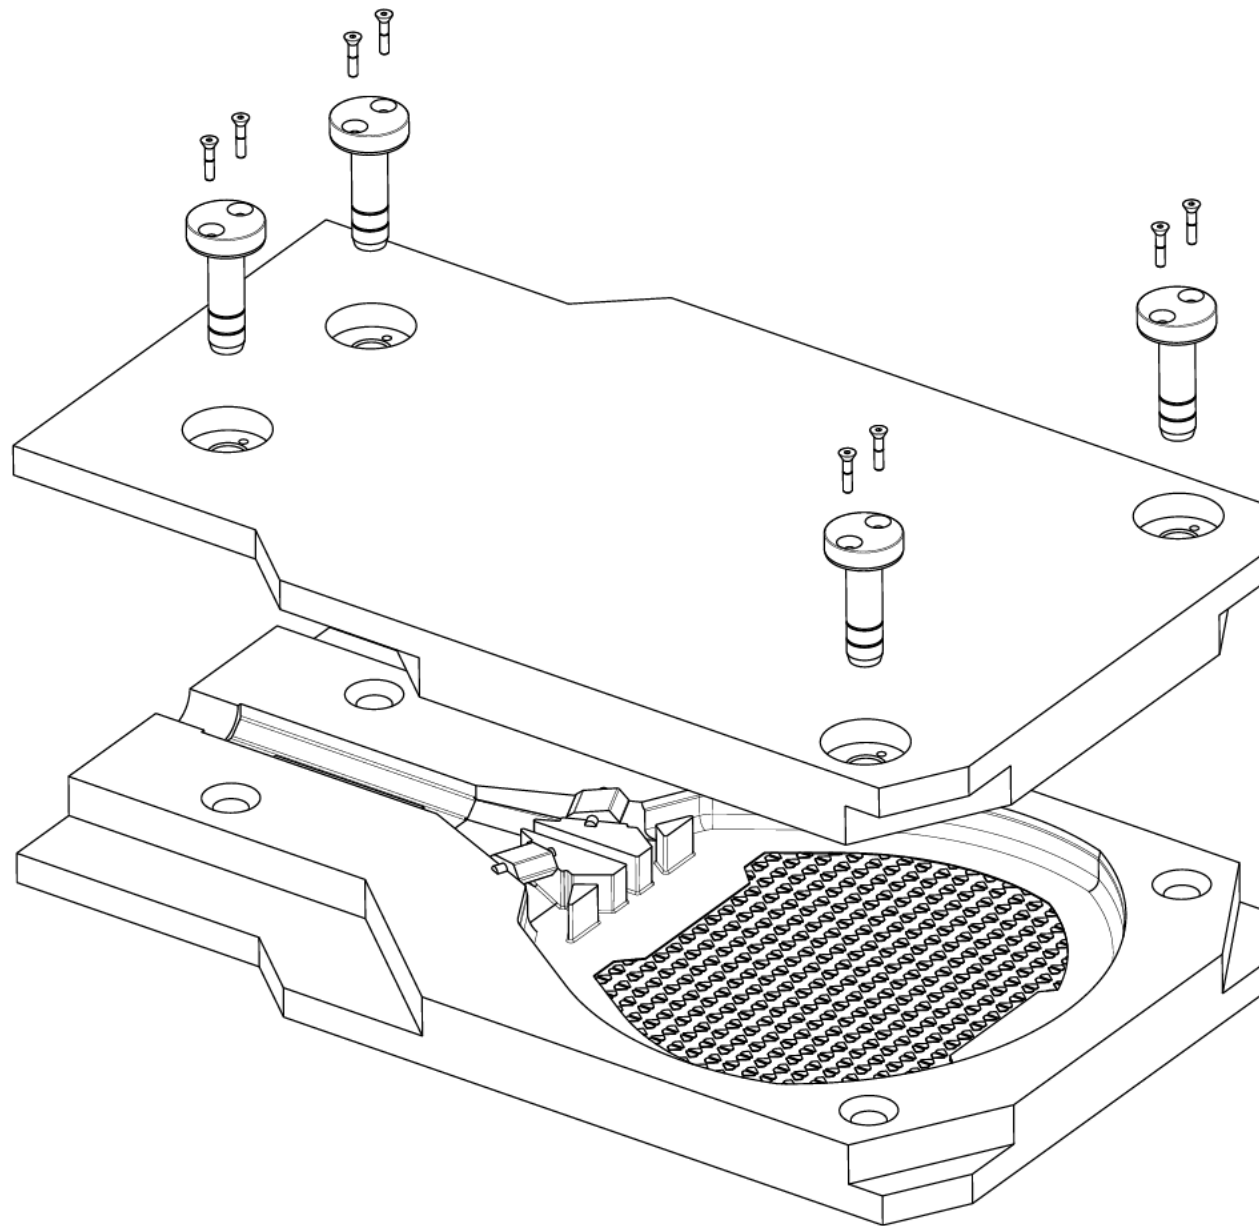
Ensamblado del conjunto. Placa superior sobre placa inferior del molde.
